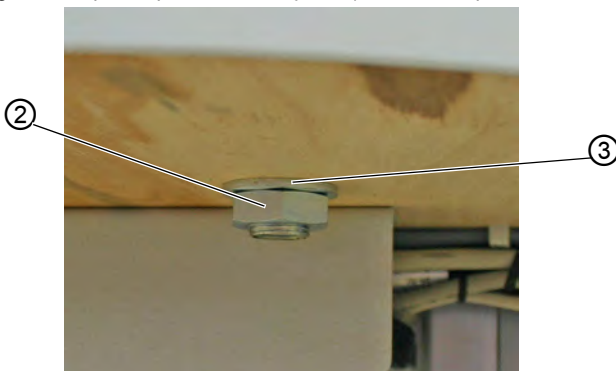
Сборка держателя катушек (верхняя сторона столешницы)
